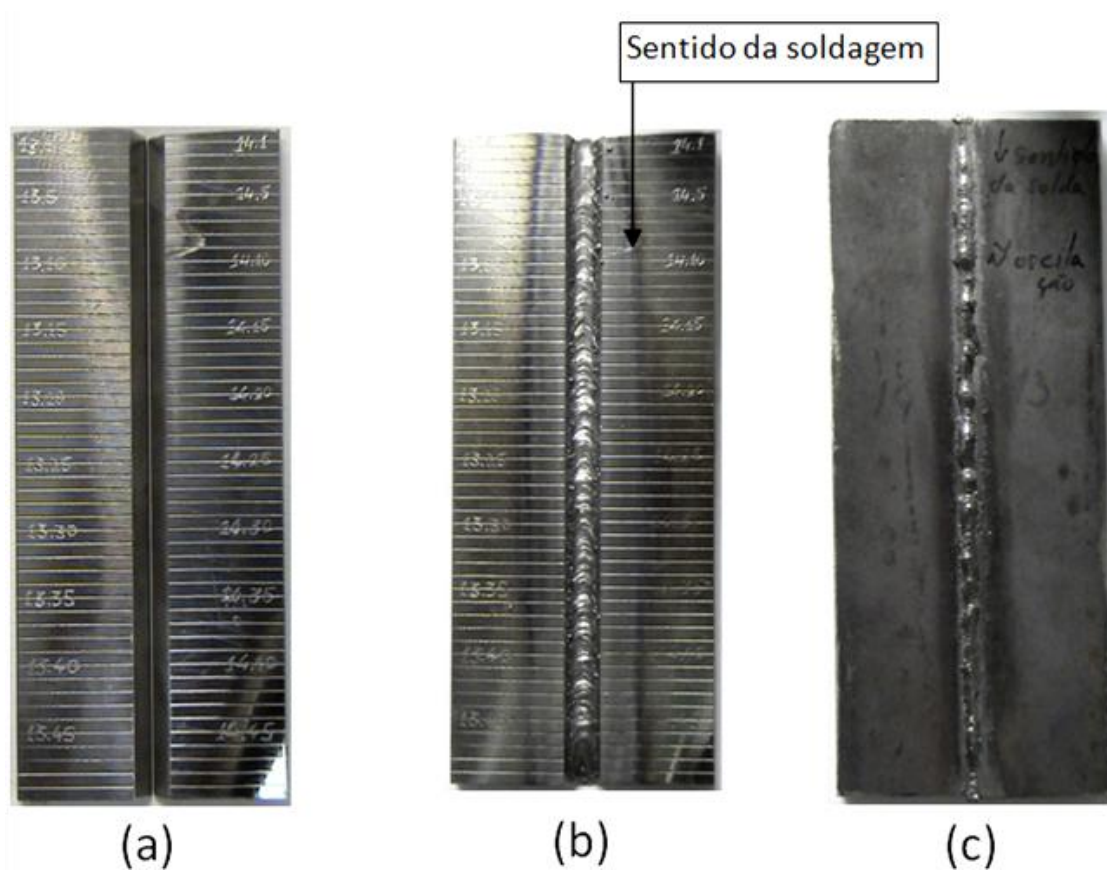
Corpo de prova “sem defeito”, soldagem não utilizando a oscilação magnética. (a) preparação; (b) cordão de solda; (c) vista inferior, cordão de solda no passe de raiz.
